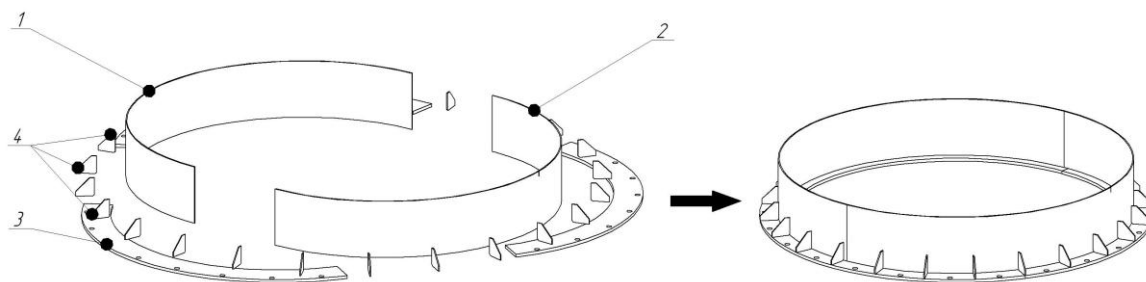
Сборка и монтаж опоры (остальное см. чертеж «595010.08.00.000 _ Опора»)
